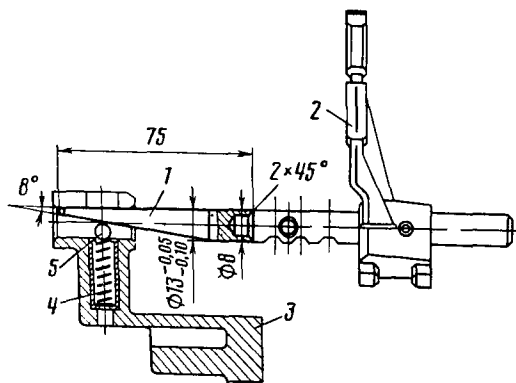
Установка штоков с вилками включения передач в корпус механизма переключения передач: 1 — оправка; 2 — шток с вилкой включения III и IV передач; 3 — корпус механизма переключения передач; 4 — пружина фиксатора; 5 — шарик
